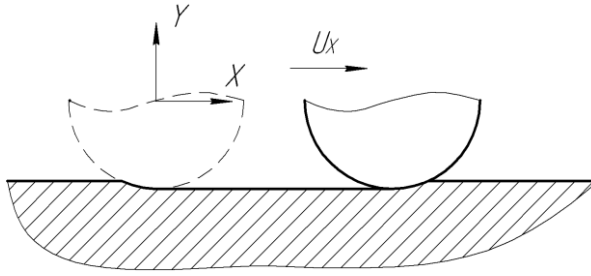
Розрахункова схема руху сферичного індентора вздовж поверхні деталі
